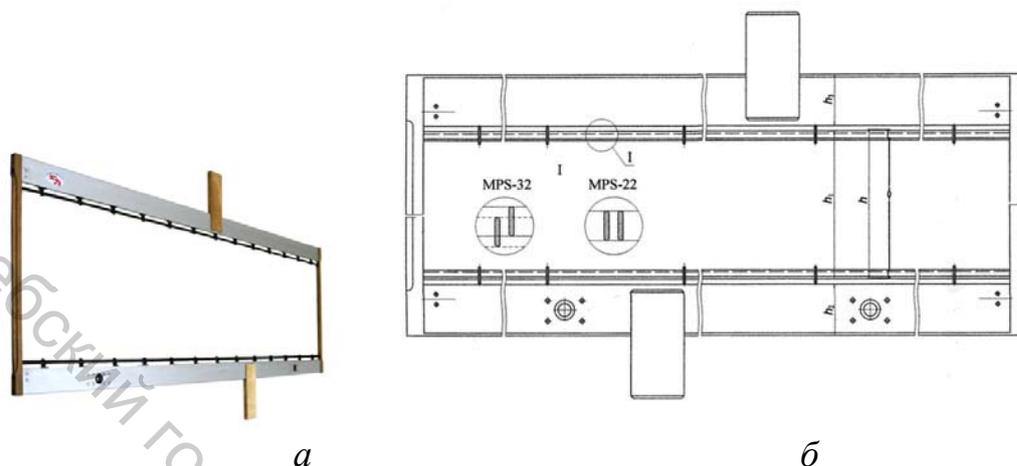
Внешний вид (а) и схема конструкции (б) ремизной рамы для ткацкого станка MPS
